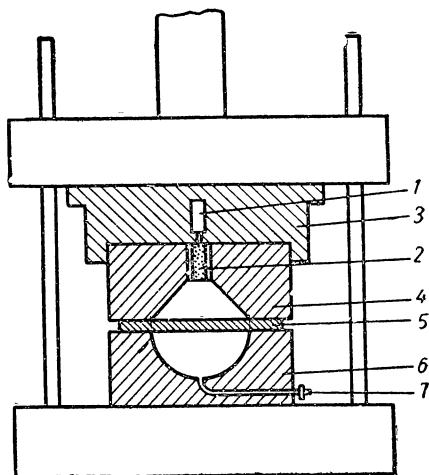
Схема формообразования заготовки из листового материала давлением газов, образующихся при взрыве: 1 — запальный механизм; 2 — взрывчатое вещество; 3 — верхняя плита пресса; 4 — верхняя часть штампа; 5 — листовая заготовка; 6 — матрица; 7 — канал для выхода воздуха.
